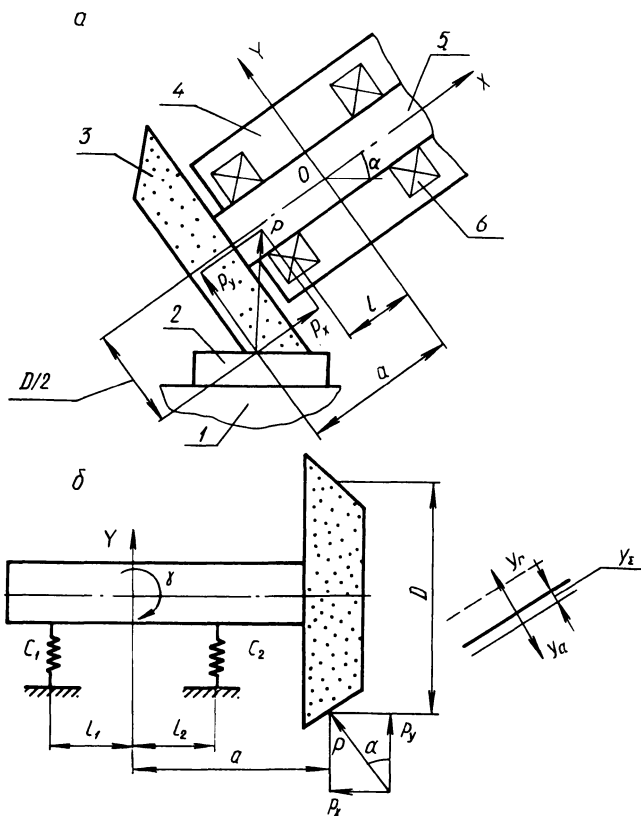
Динамическая система плоскошлифовального станка новой компоновки: а – схема действия составляющих силы резания; б – динамическая схема шпиндельного узла; 1 – стол; 2 – обрабатываемая деталь; 3 – шлифовальный круг; 4 – шпиндельный узел; 5 – шпиндель; 6 – опора шпинделя
